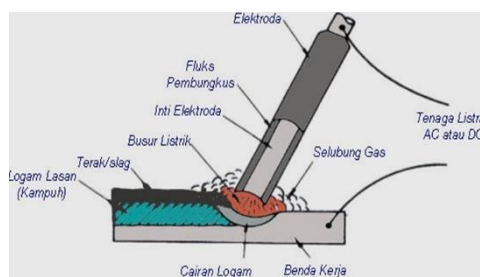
8 Skematik las *Flux-Cored Arc Welding
